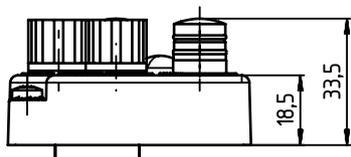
Desenho dimensional BPS com tampa de conexão MK 348
